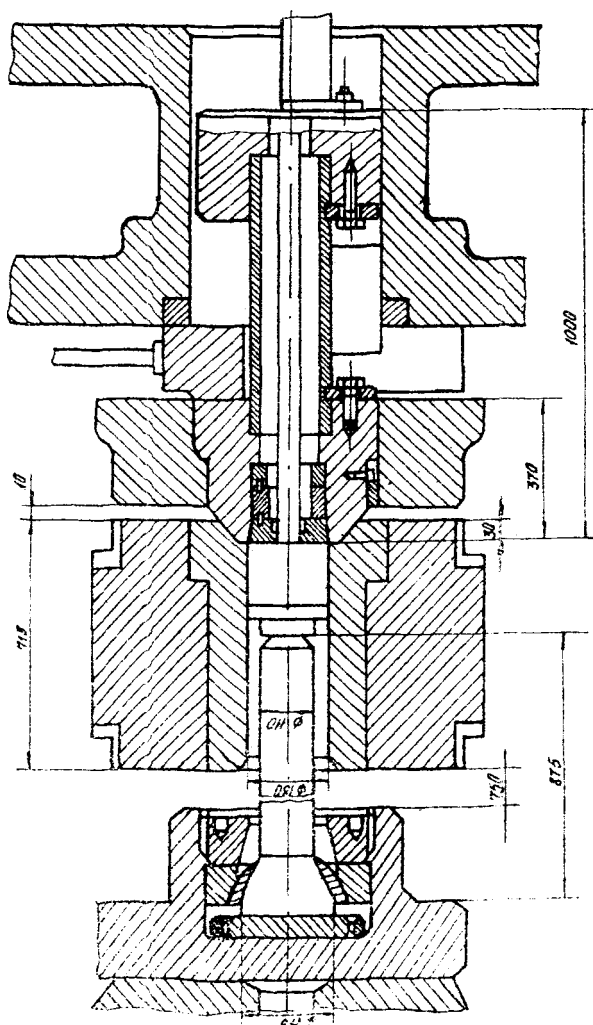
Наладка инструмента для прессования профилей на прессах 12 мм, 20МН
